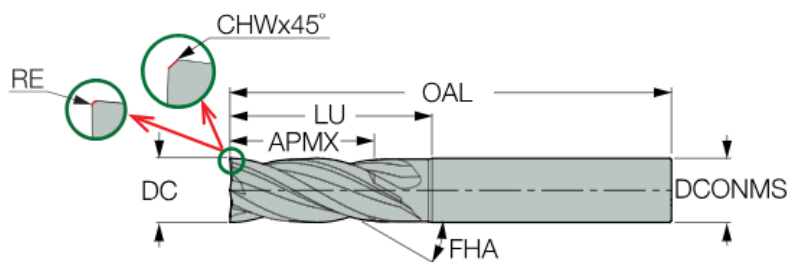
Ескіз до обробки на операції 065 – фрезерну з ЧПК
